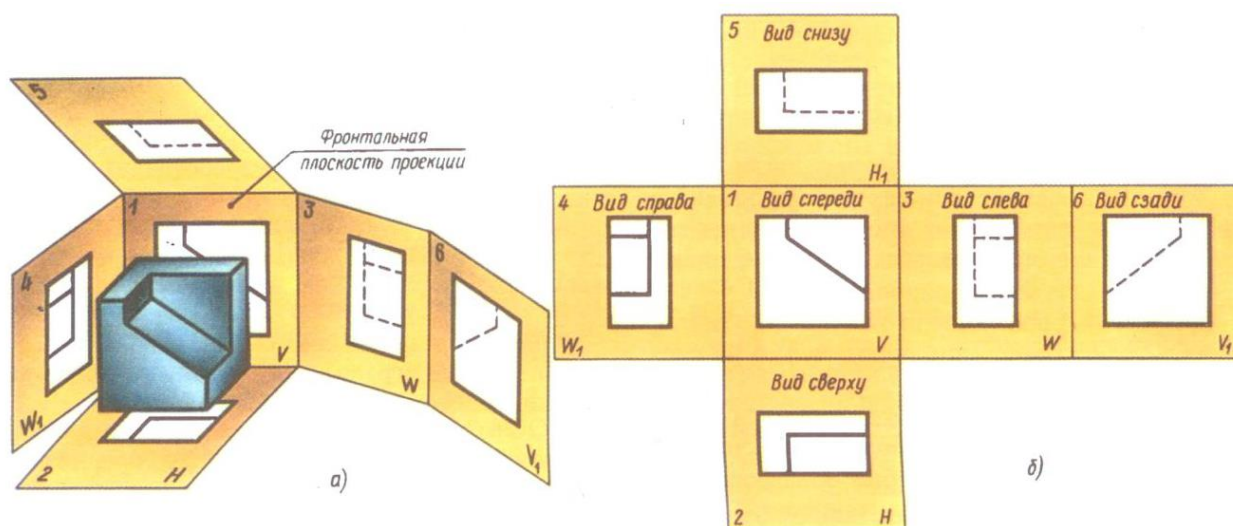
Основные виды: 1- вид спереди (главный вид); 2- вид сверху; 3- вид слева; 4- вид справа; 5- вид снизу; 6- вид сзади
